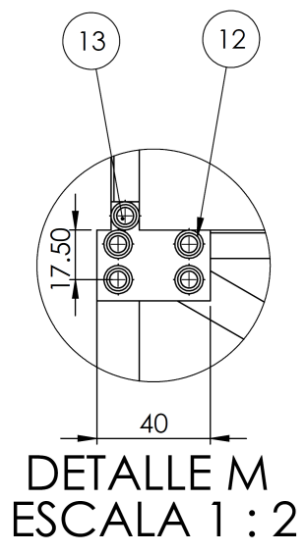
10: Vista de detalles M del ensamblaje del soporte 3. Fuente: Elaboración propia.
